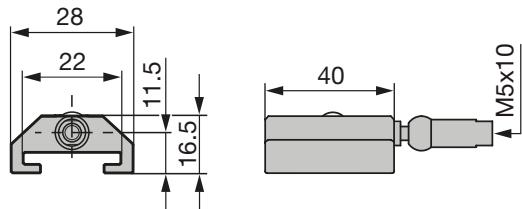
Medidas de montaje del sensor de posición BTL5-T-2814-1S
